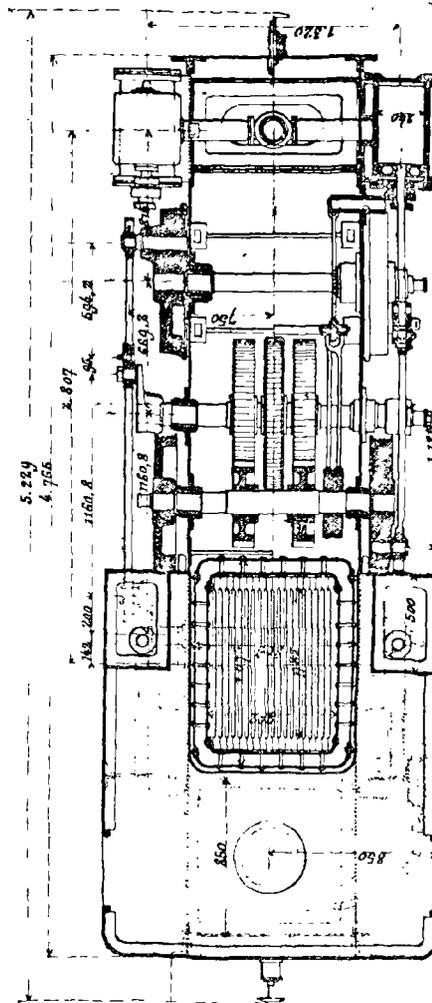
Plan de la machine du chemin de fer de Friederichsseen à la Lahn.
